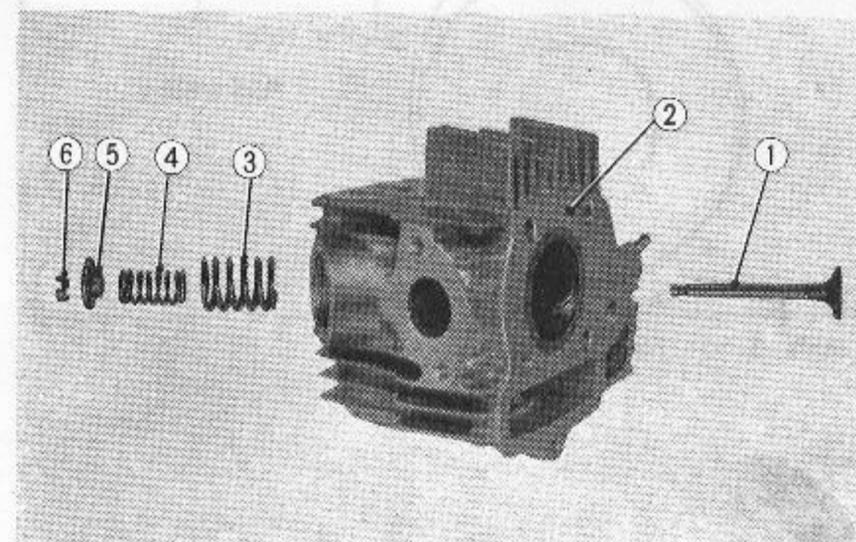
B Zylinderkopf mit Einlaßventil
